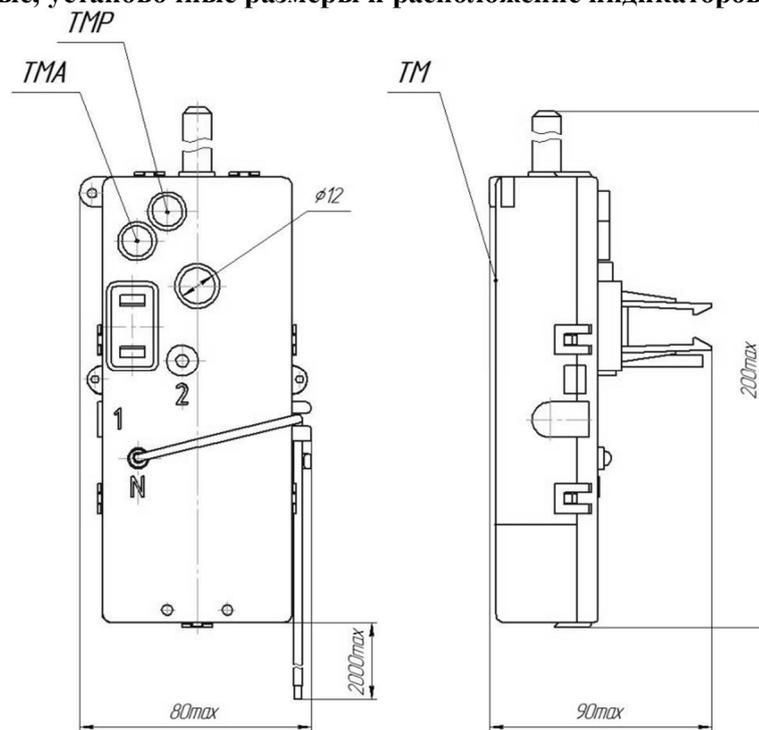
Габаритные, установочные размеры счетчиков в корпусе «тип I»
